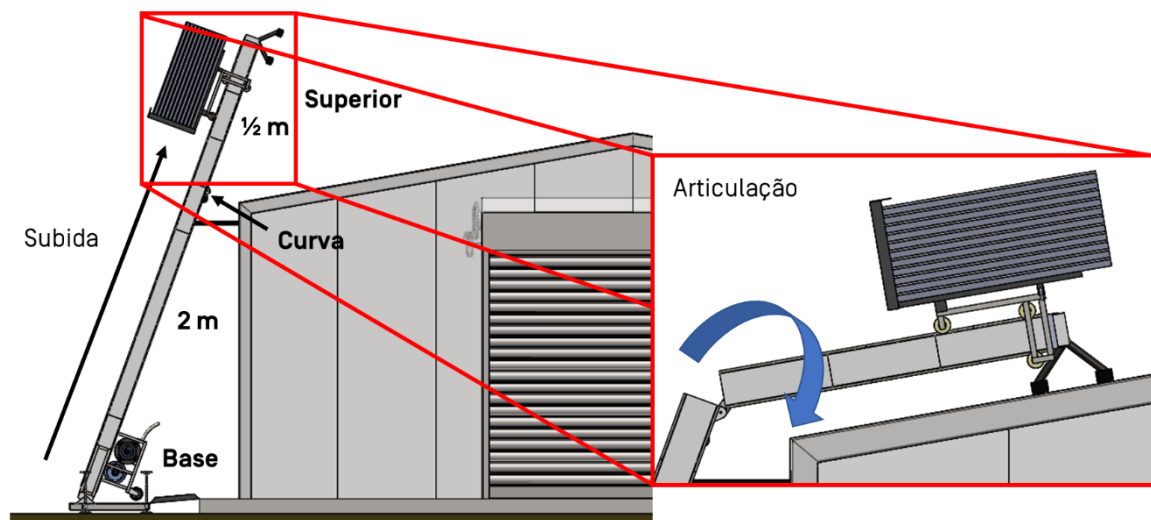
Elevador de cargas [subida e articulação] – modelo CAD 3D.
